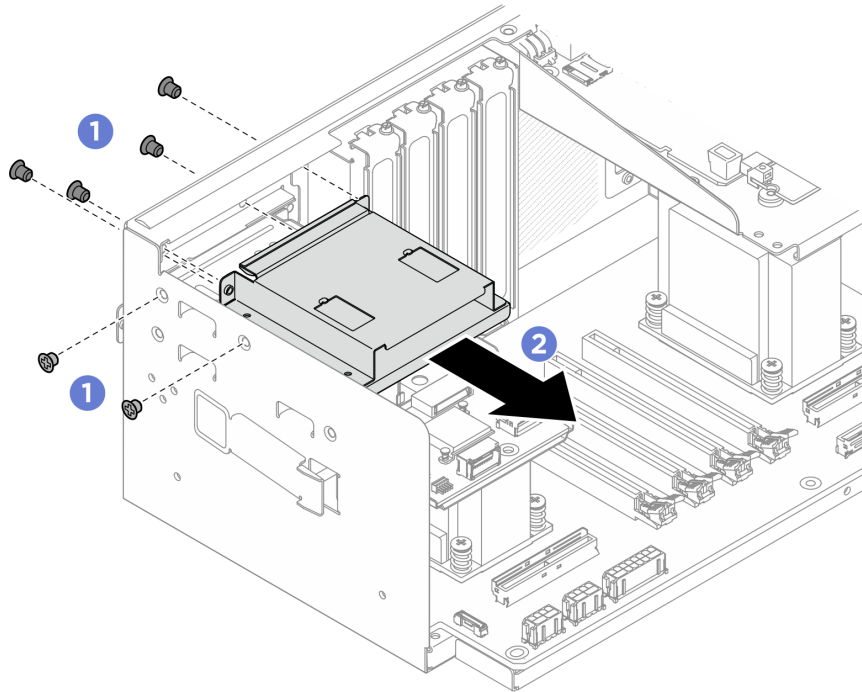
Entfernen des Gehäuses der integrierten Diagnoseanzeige
